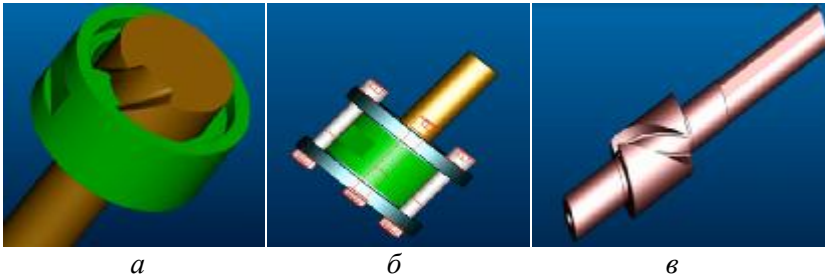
а* – схема притирки калибра; *б* – приспособление; *в* – контркалибр
